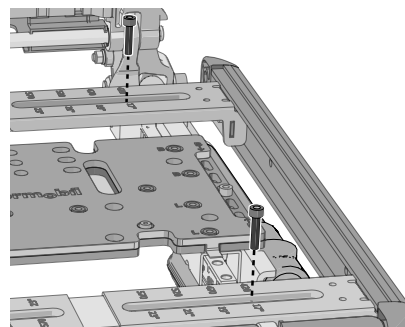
Die beiden Sitzplattenhalterungen sind mit zwei Schrauben befestigt.
